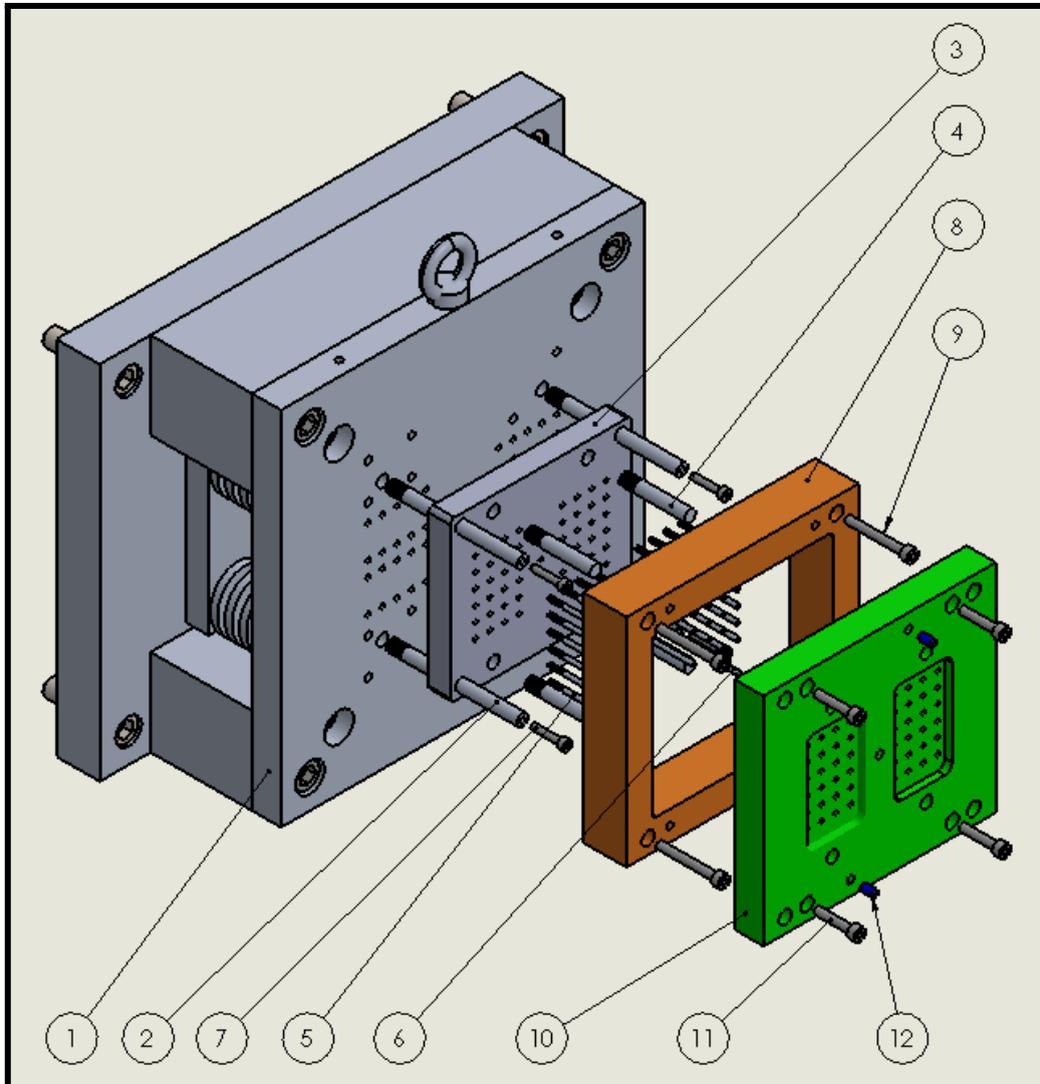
M. Vista explosionada de la configuración 4 del portamolde
